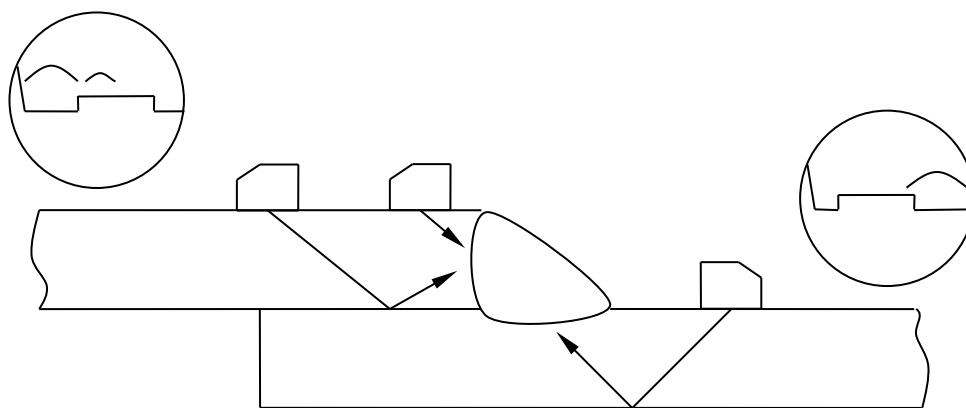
Схема контроля нахлесточных сварных соединений
